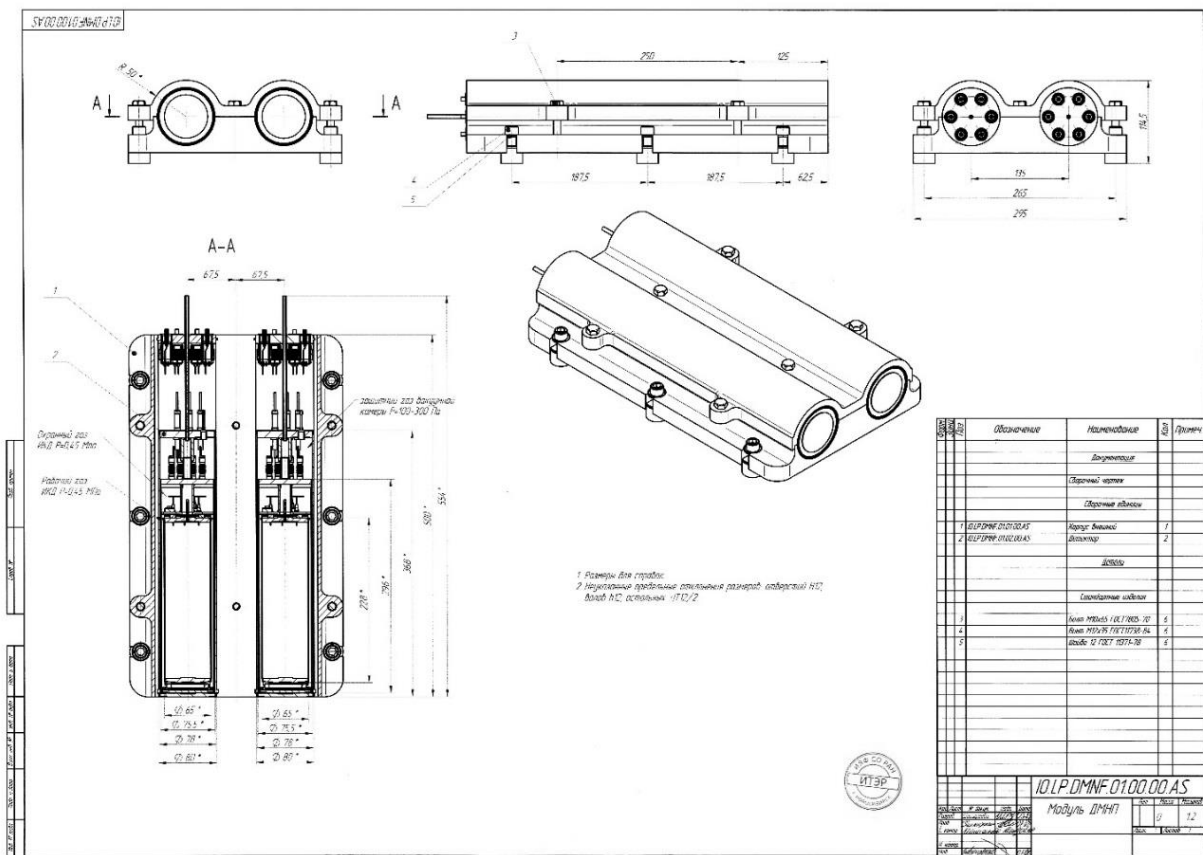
Сборочный чертеж новой конструкции модуля ДМНП
